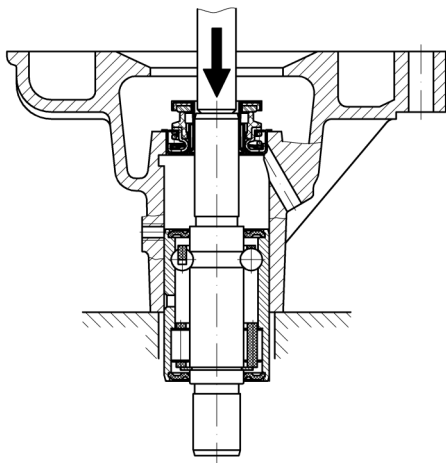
Выпрессовка подшипника с валиком водяного насоса
